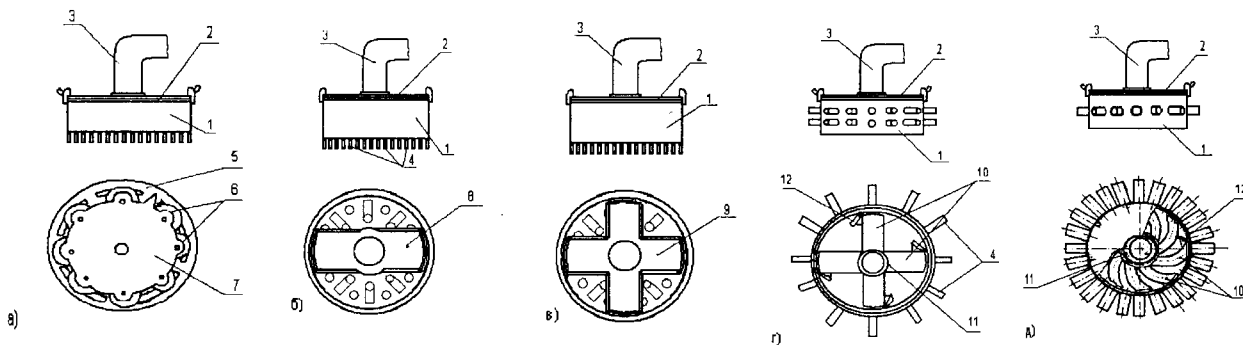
Распределительные головки с измельчительными аппаратами: 1 – корпус головки; 2 – крышка головки; 3 – нагнетательный патрубок; 4 – выливной штуцер; 5 – сменная противорежущая пластина с продолговатыми щелями; 6 – дисковые ножи; 7 – ротор; 8 – ротор с режущими кромками; 9 – крестообразный ротор с режущими кромками; 10 – патрубки ротора; 11 – стакан ротора; 12 – нож
